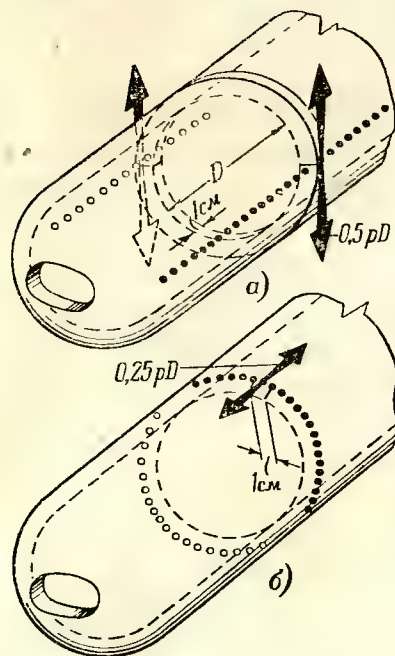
Схема действия сил, стремящихся разорвать котельный барабан.
